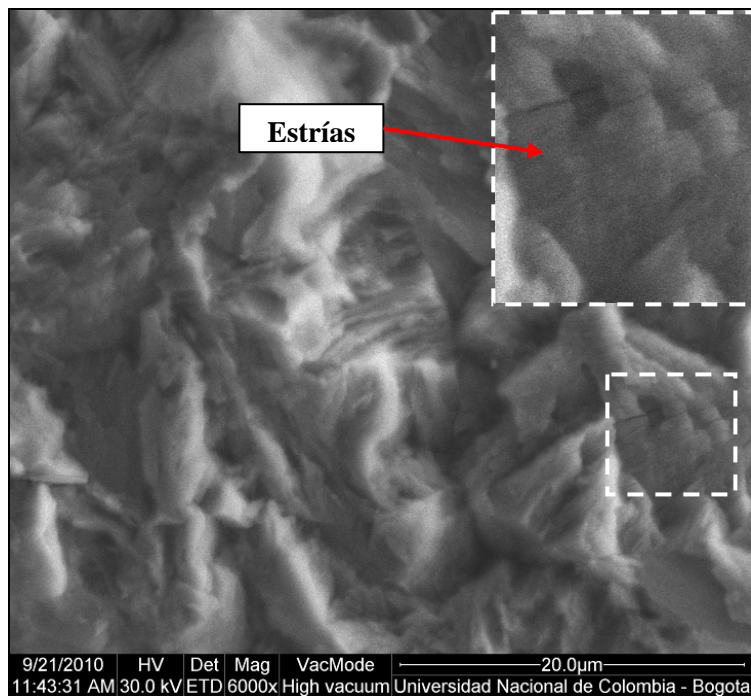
Detalle de la zona 2, zona de interfaz. SEM. 1600X.
